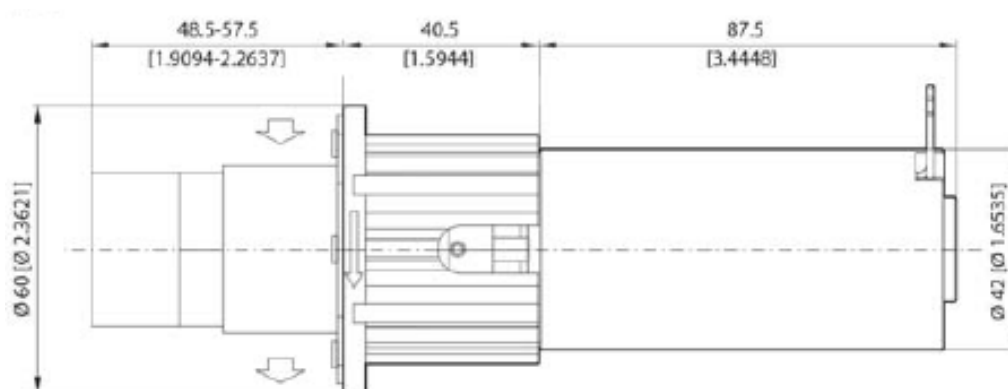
Dimensões da bomba selecionada (Clark Solutions, n.d.)
